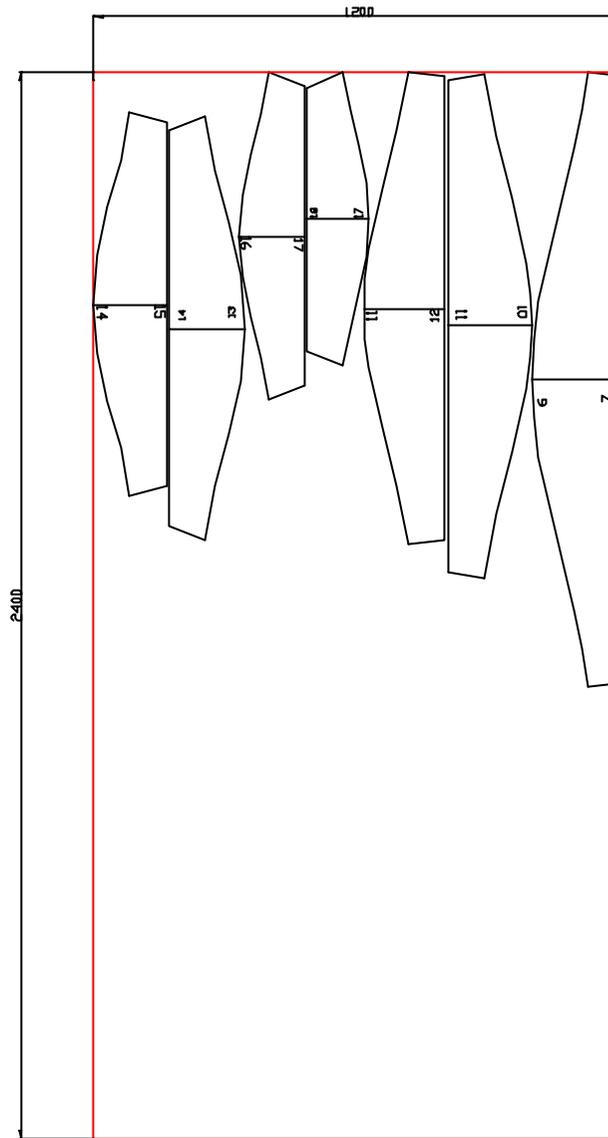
Ubicación de las plantillas de la espiral en la plancha de acero para el trazado y oxicorte (Segmentos indicados)
